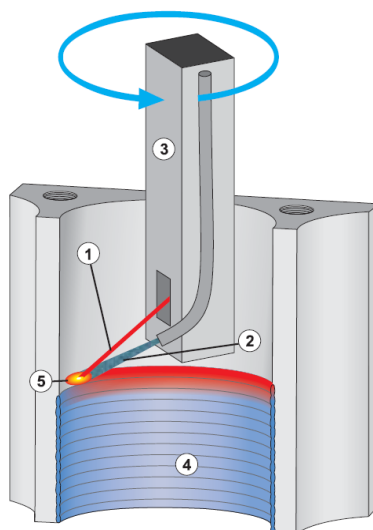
Схематическое изображение процесса лазерного легирования поверхности цилиндра кремнием: 1 – лазерный луч, 2 – струя порошка, 3 – вращающееся лазерное оптическое устройство, 4 – легируемый слой, 5 – оплавляемая зона [21]
